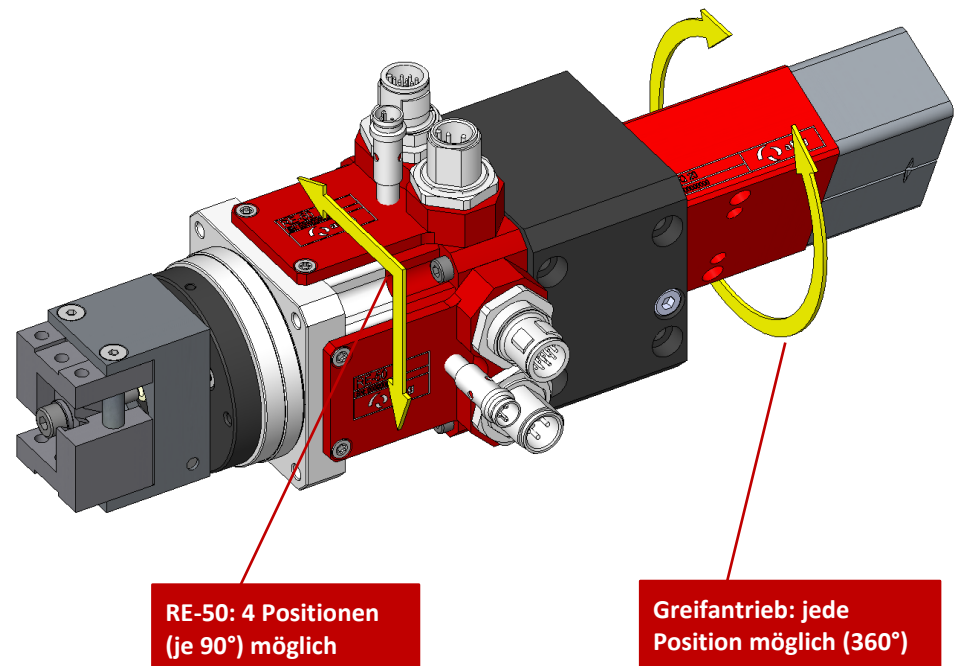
Anpassungsmöglichkeiten für Kabelanschlüsse
